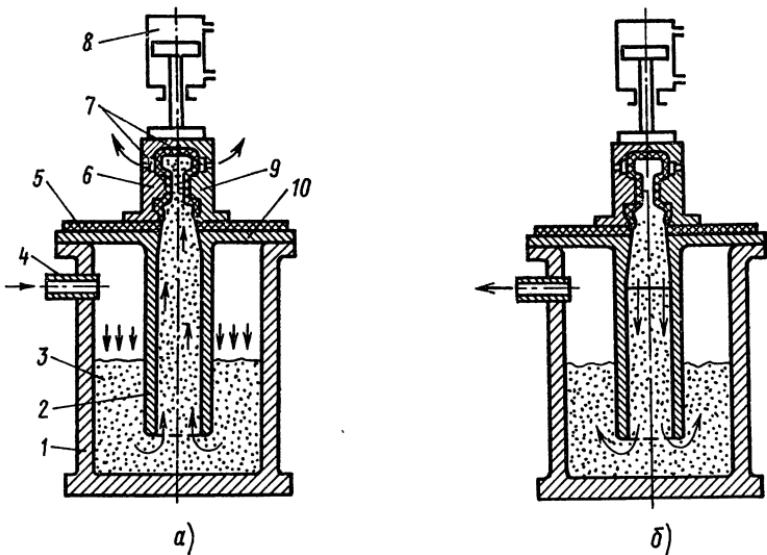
Пескодувная установка для изготовления оболочковых стержней с надувом плакированной песчано-смоляной смеси снизу:
